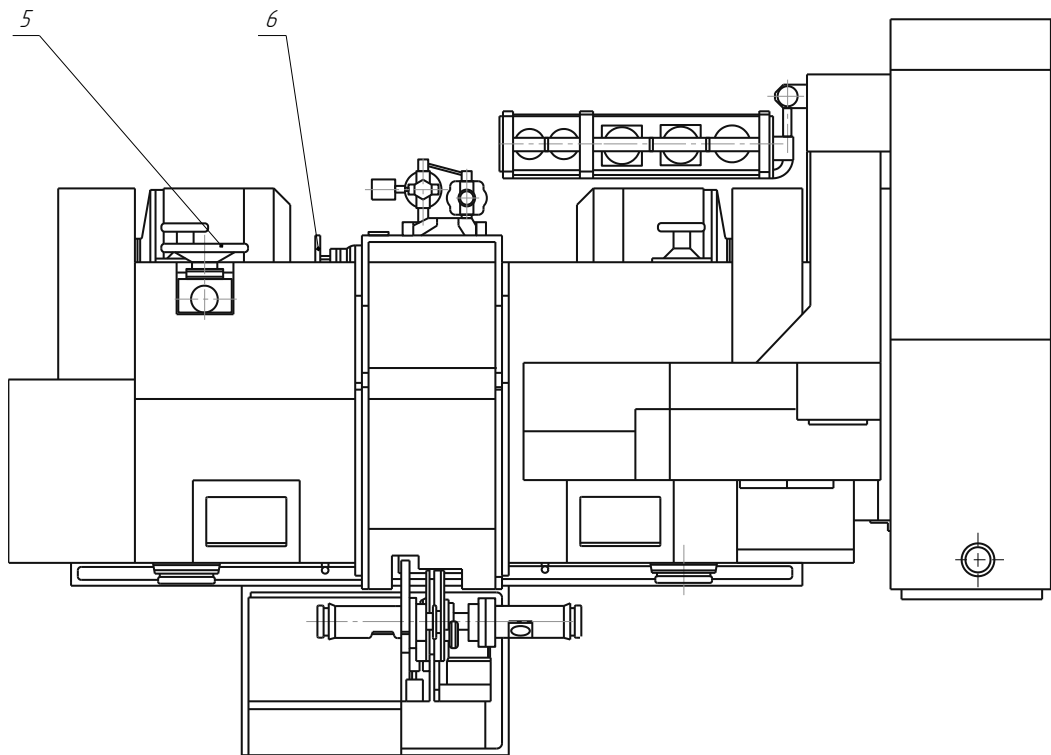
Загальний вигляд автомату (вид зверху)
